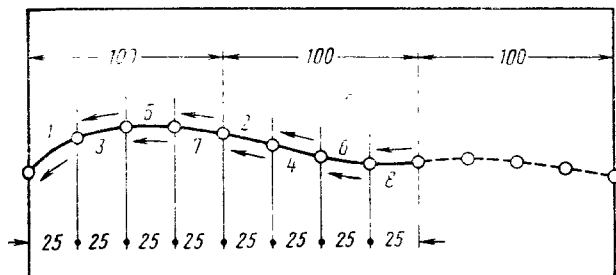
Обратнo-ступенчатый способ сварки
